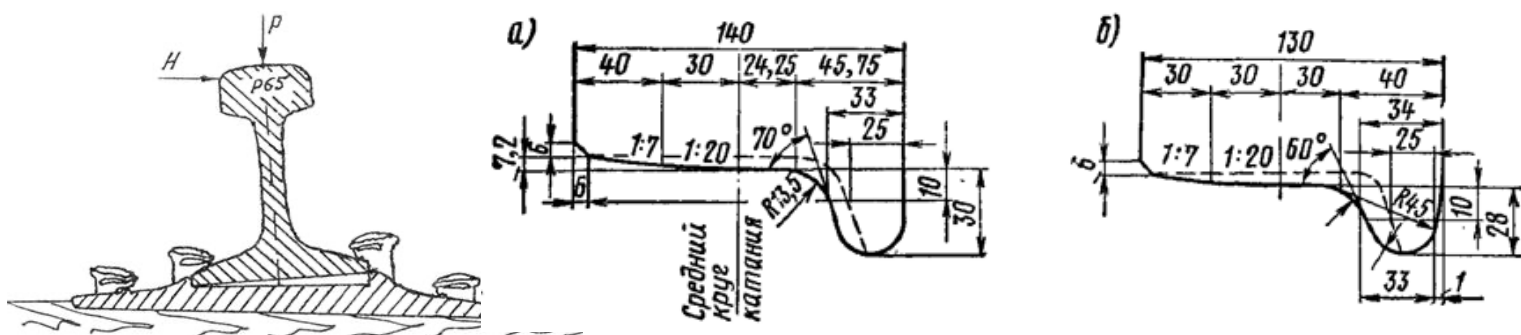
Очертания и основные размеры ободов колес: а – локомотивного; б – вагонного
